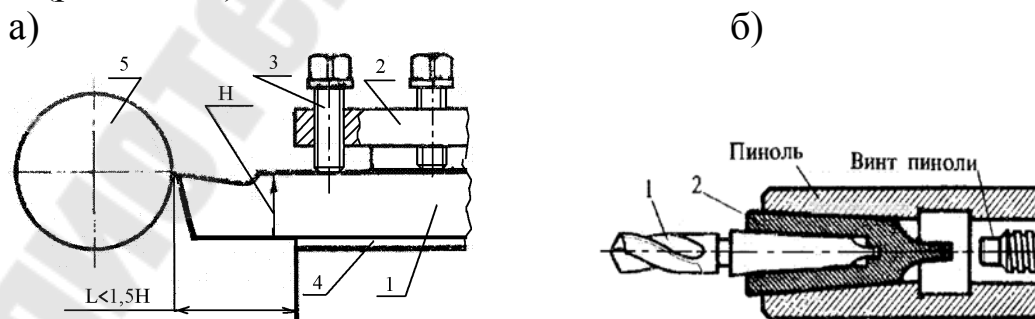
Схемы закрепления инструмента на токарном станке
